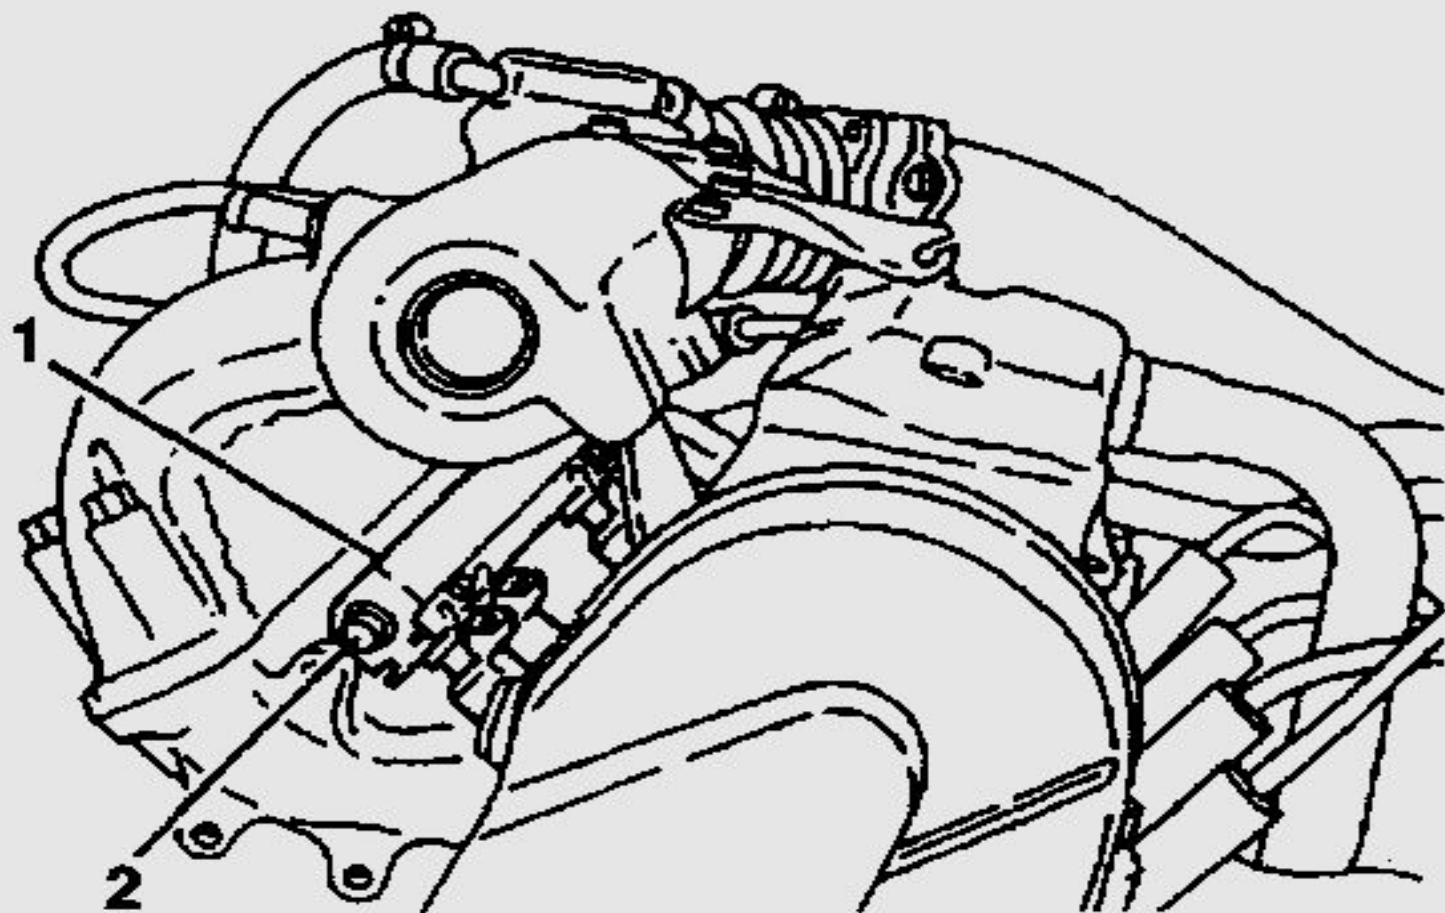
Расположение рампы форсунок: 1 - рампа форсунок; 2 - штуцер для контроля давления топлива
